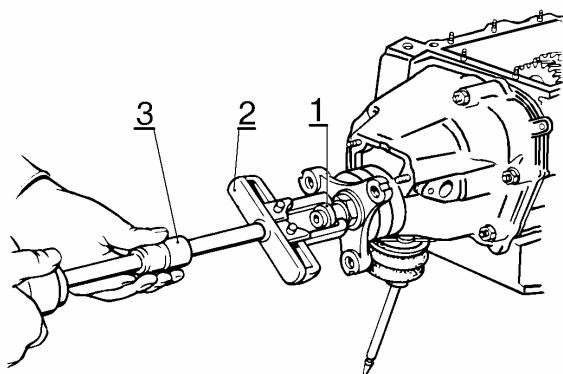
Снятие центрирующего кольца с конца вторичного вала:
